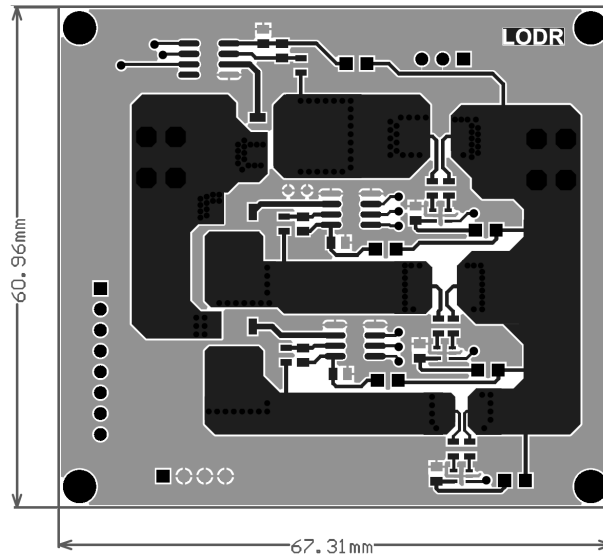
3D model testovacího modulu - spodní vrstva
